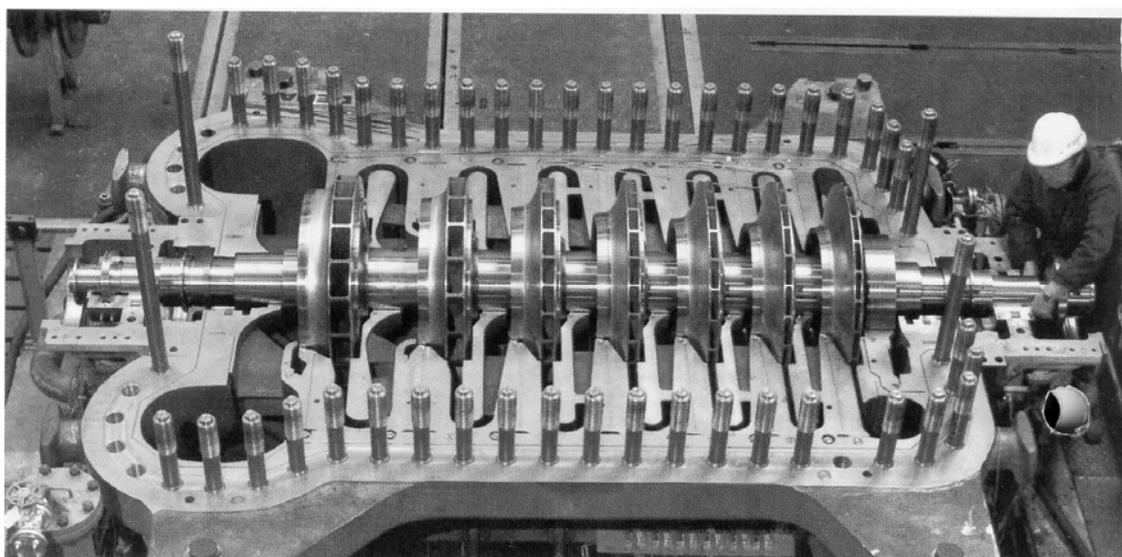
Семиступенчатый одновальный центробежный компрессор для одного из химических производств (верхняя часть корпуса снята)
